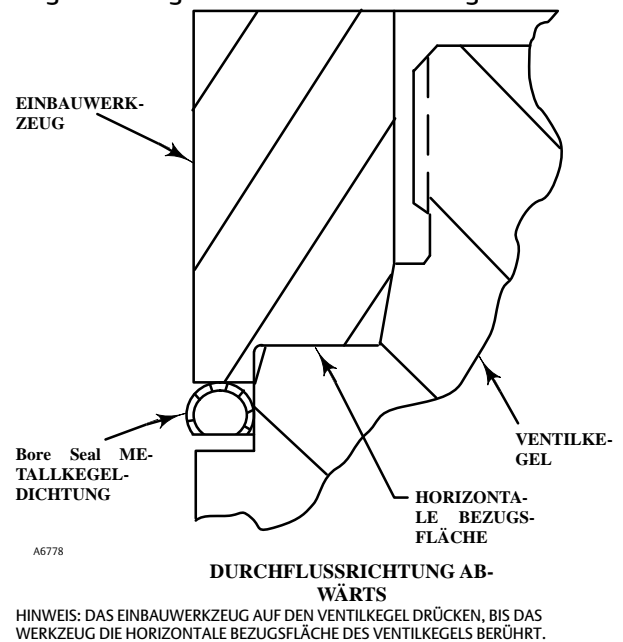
Installieren der Bore Seal Kegeldichtung mit dem Einbauwerkzeug
